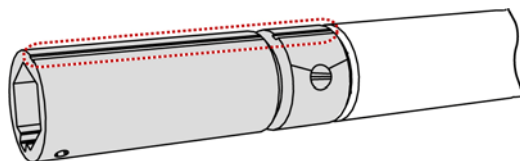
Маркировка (длинный паз) на приводном рычаге с установленным адаптером
